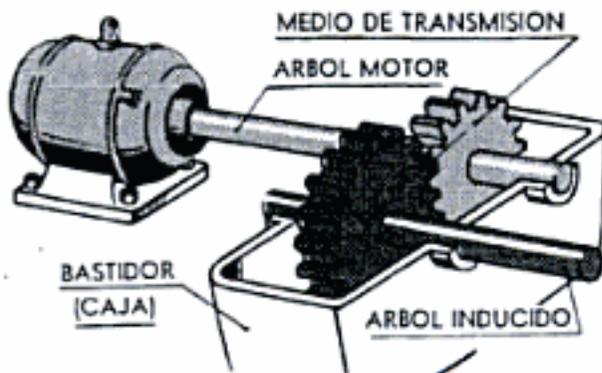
,1 Elementos principales de un mecanismo de engranaje.
